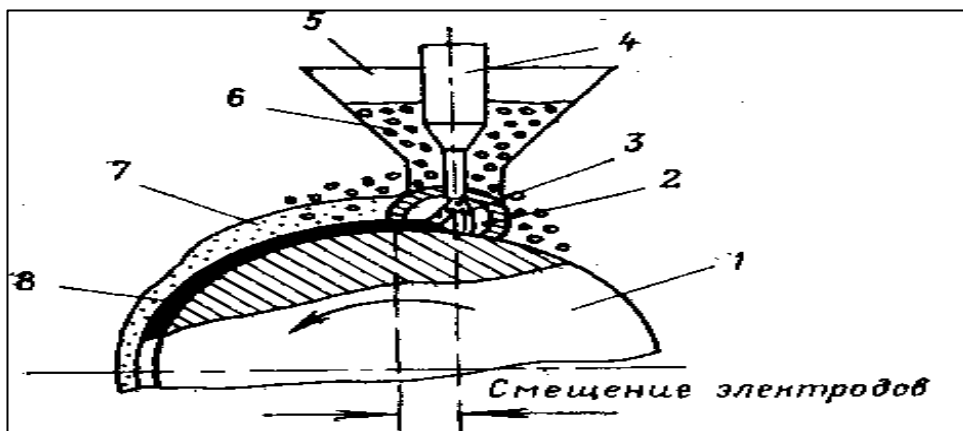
Схема наплавки деталей под слоем флюса:
